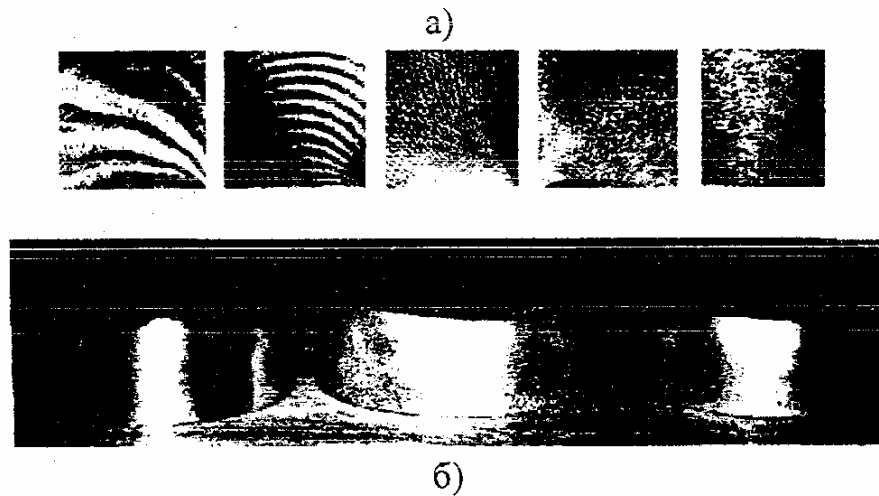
Фотографии макрорельефа (а) поверхности образцов из алюминиевых сплавов марки АМГ3 после различных режимов обработки: 1 - 250 об/мин; 2 - 325 об/мин; 3 - 410 об/мин; 4 - 630 об/мин; 5 - 840 об/мин; вид поверхности деталей после иглофрезерования и абразивной обработки (б). При обработке деталь вращается вокруг своей оси и ось поворачивается от 0 до 80° (рис. 2).
